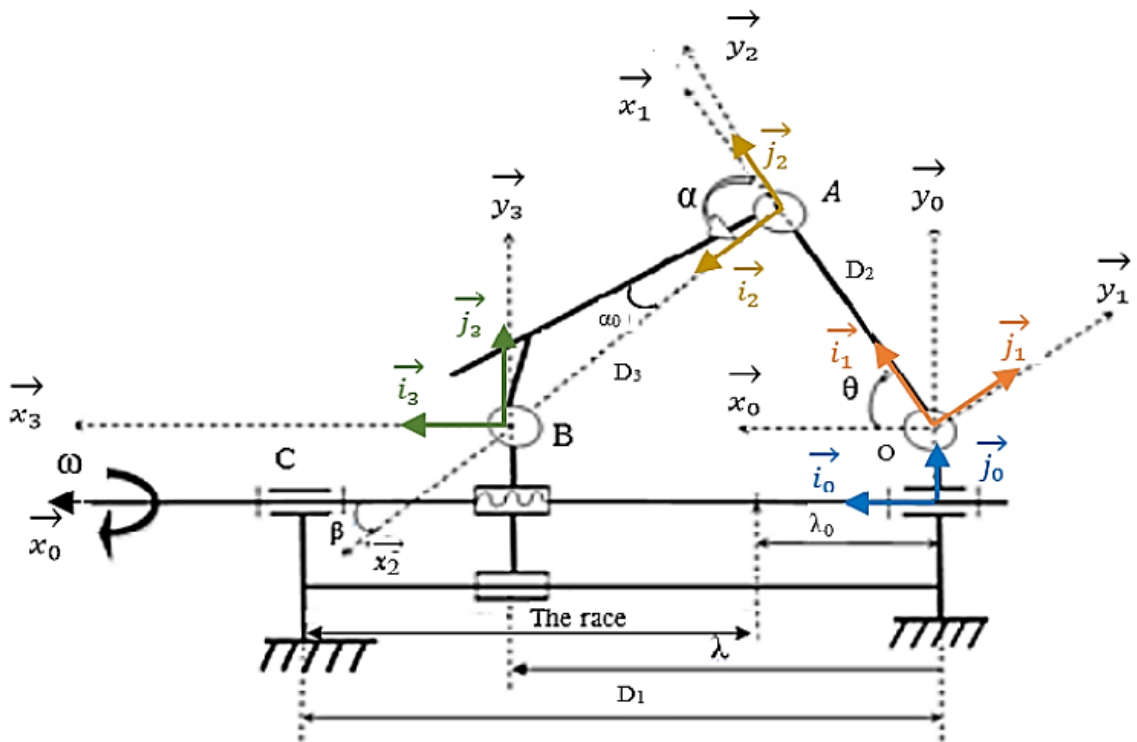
Mécanisme et chaîne cinématique de la machine
